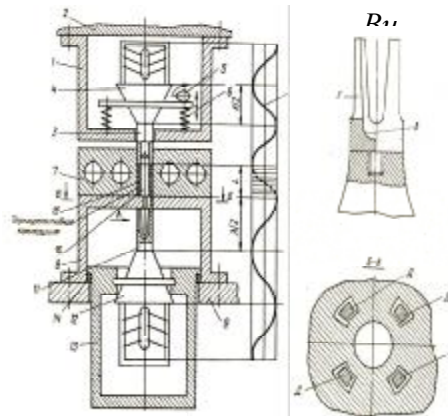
Схема пристрою для нанесення полімерної композиції:
